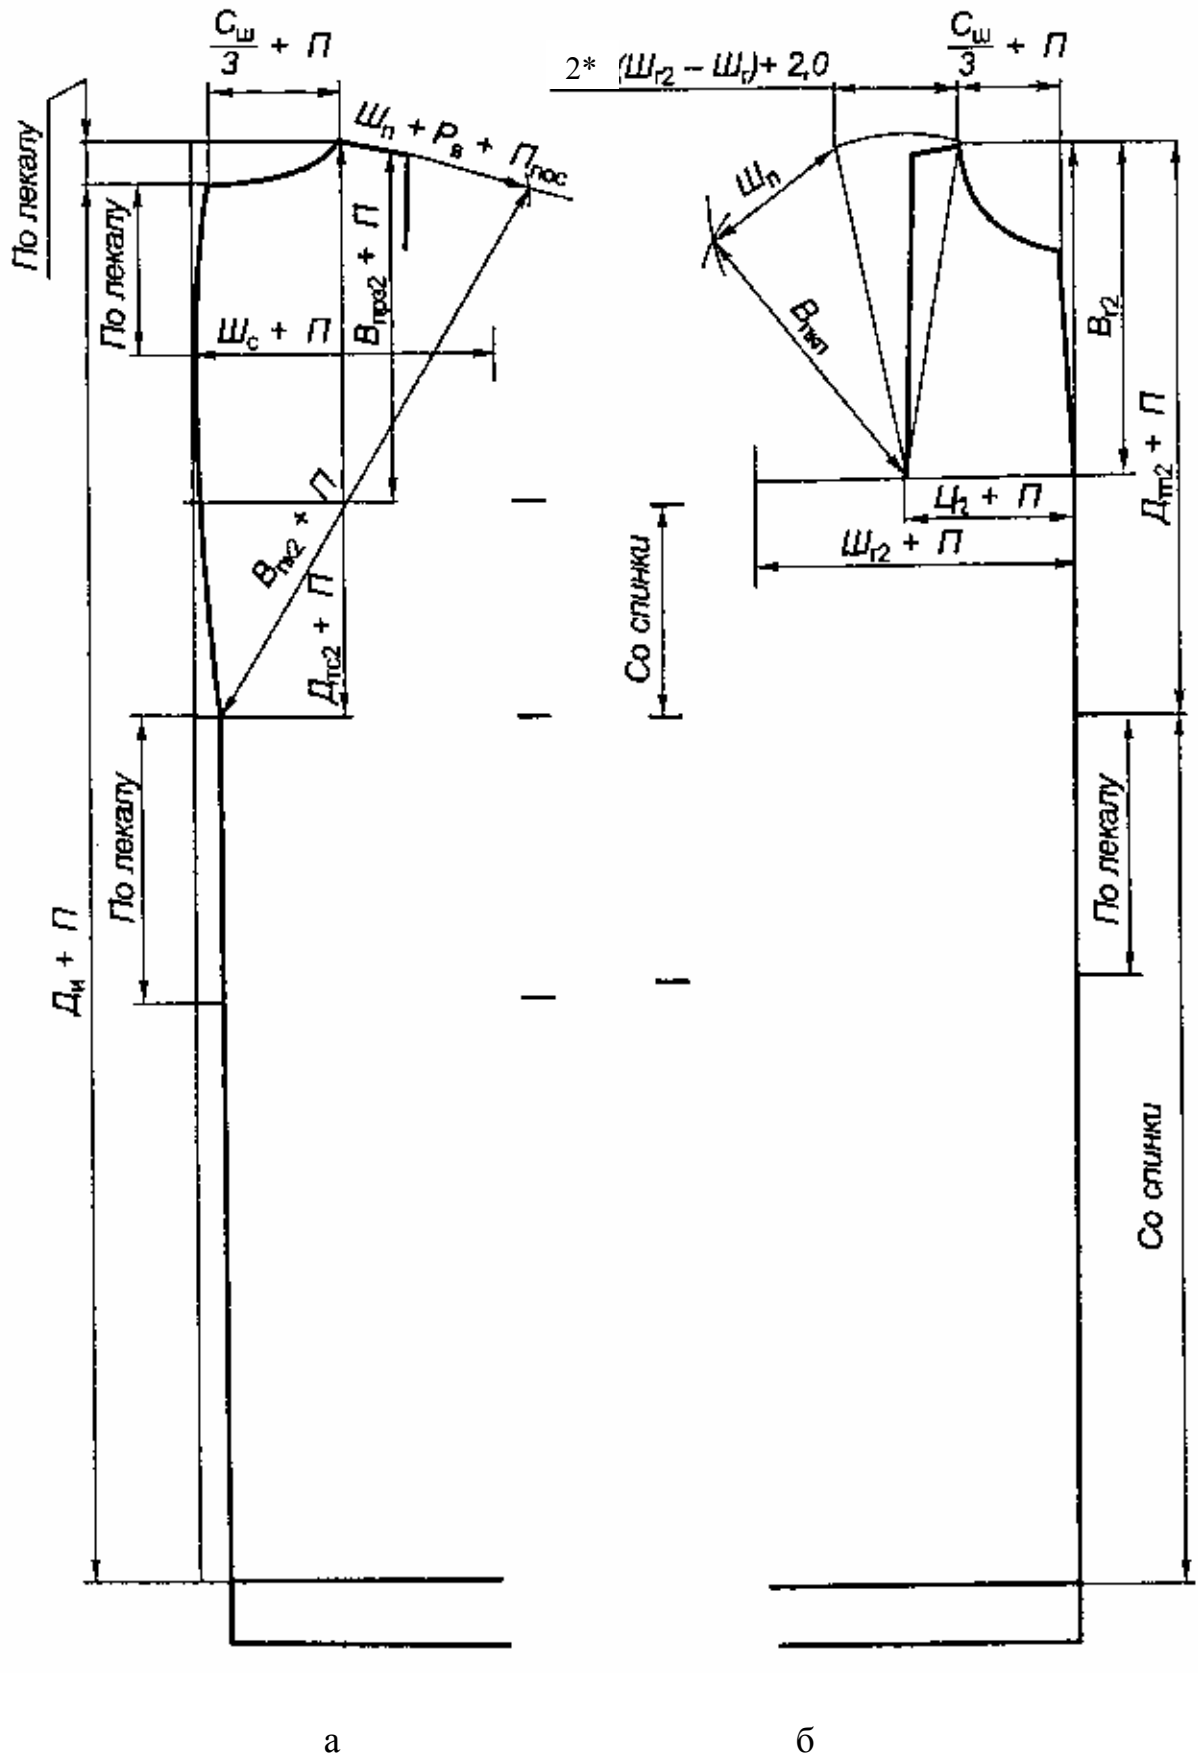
Намелка деталей спинки (а) и переда (б) женской одежды по лекалам базовых конструкций
